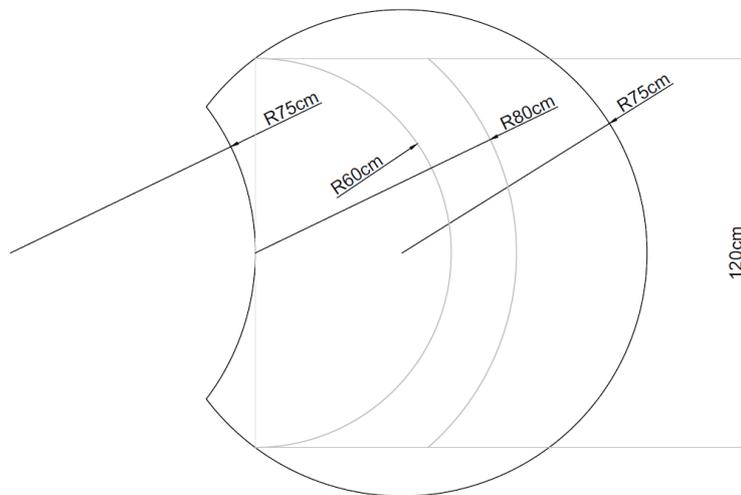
Dimensiones tablero. Fuente: AutoCad
